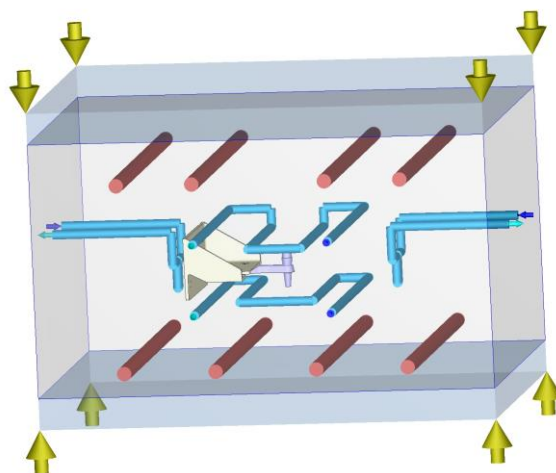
Conjunto criado para a simulação. (Moldex3D Designer).
